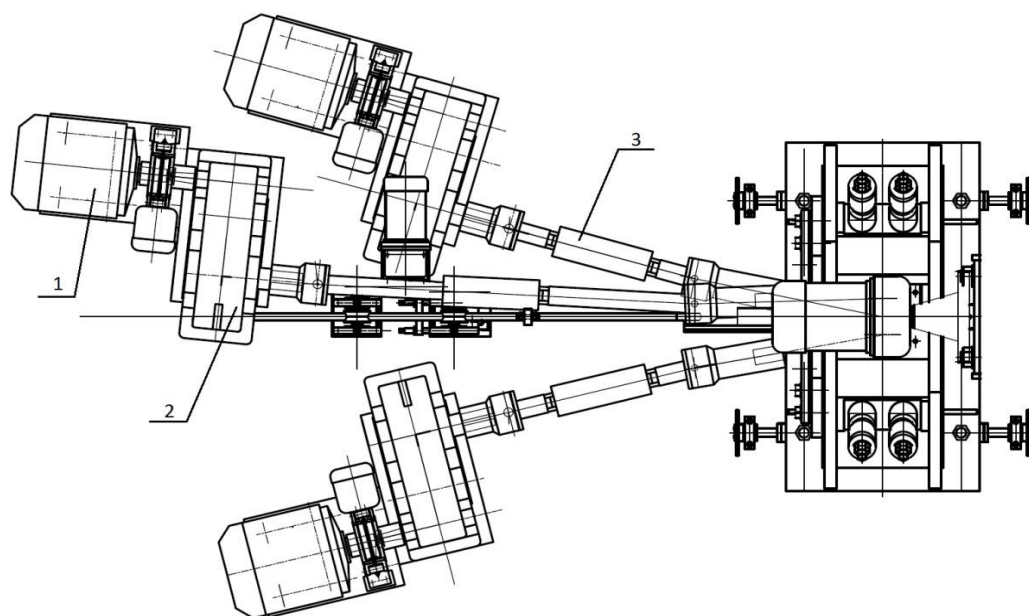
Главный привод клетки прошивного стана: 1 – электродвигатель; 2 – редуктор;
